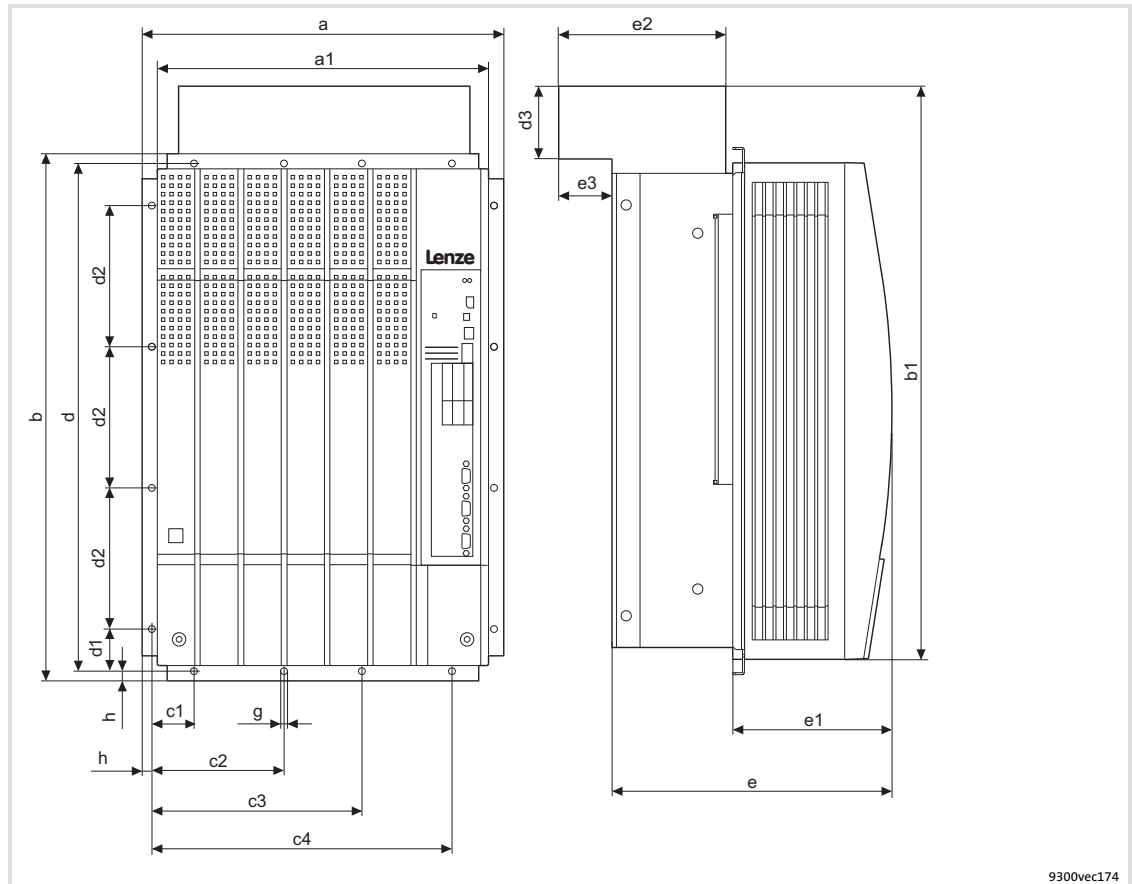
Abmessungen Montage thermisch separiert 55 kW
